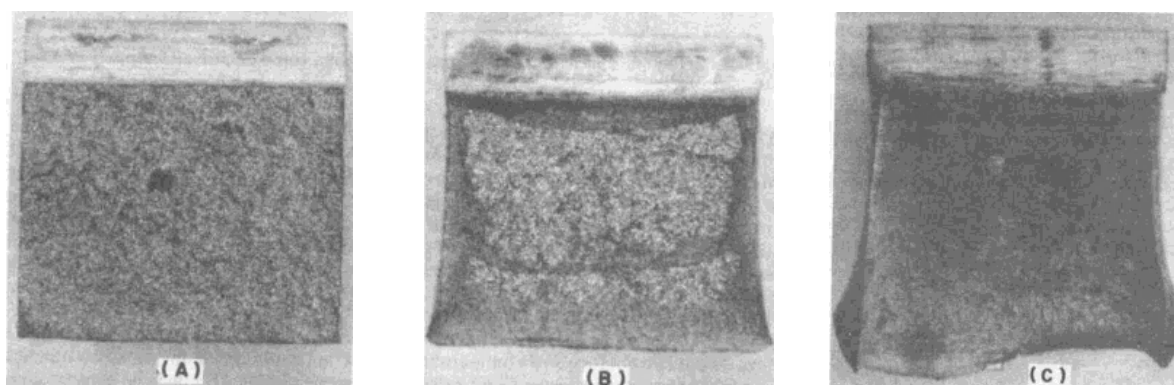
Superfícies típicas de fratura de um ensaio Charpy.[8]
